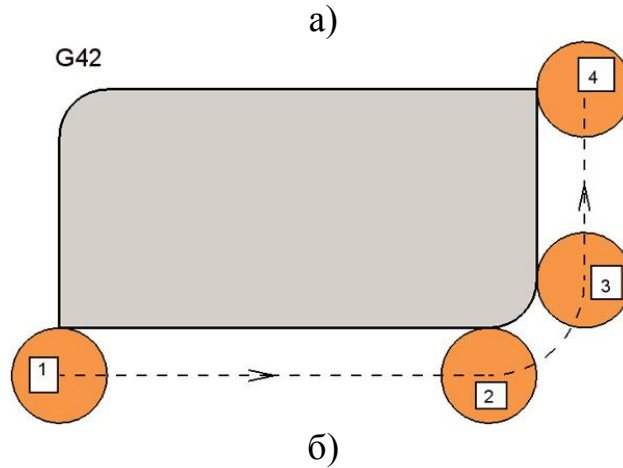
Траєкторія обробки заготовки фрезою 9 мм
